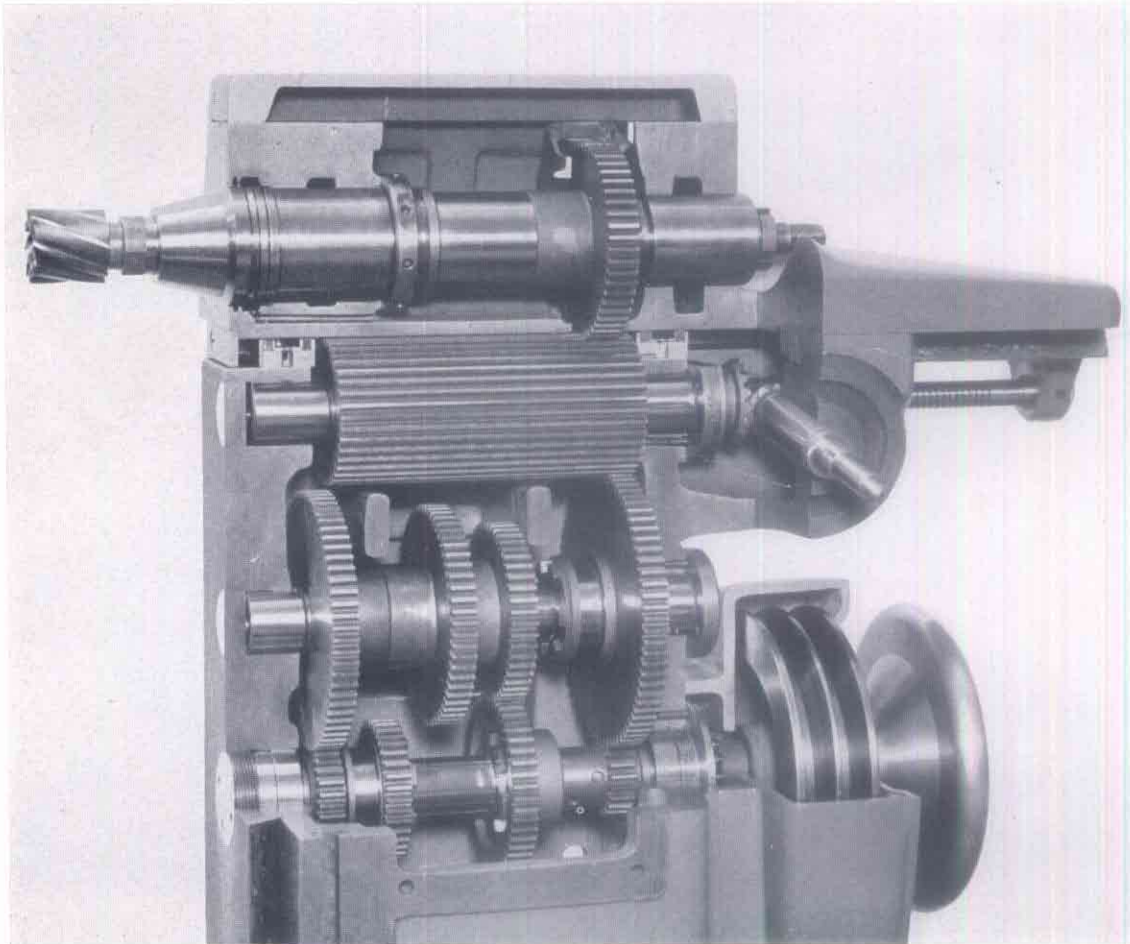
Schnitt durch Hauptgetriebe und Waagrechtfrässpindel
